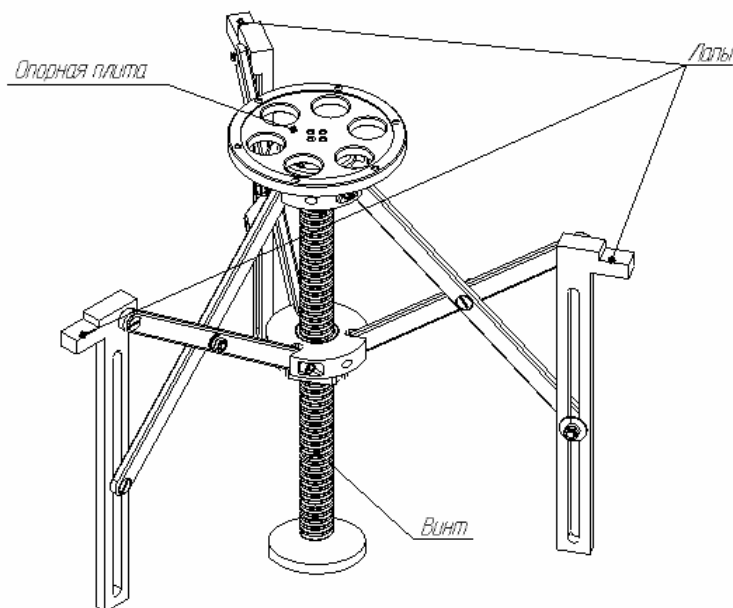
Сборочно-сварочное приспособление для сборки патрубка и днища
